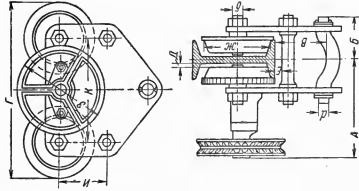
Двухкатковая кошка с ручным механизмом передвижения.
